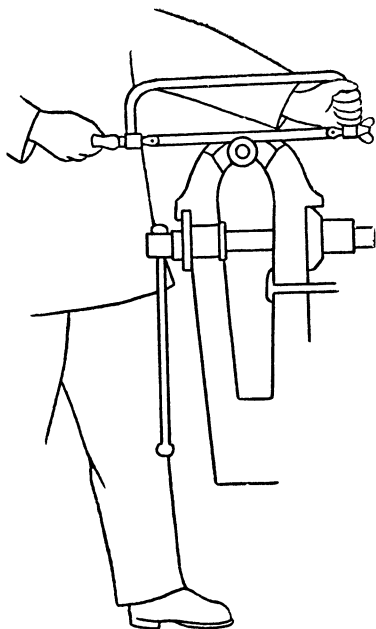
Положение корпуса и рук при резке металла ножовкой.
